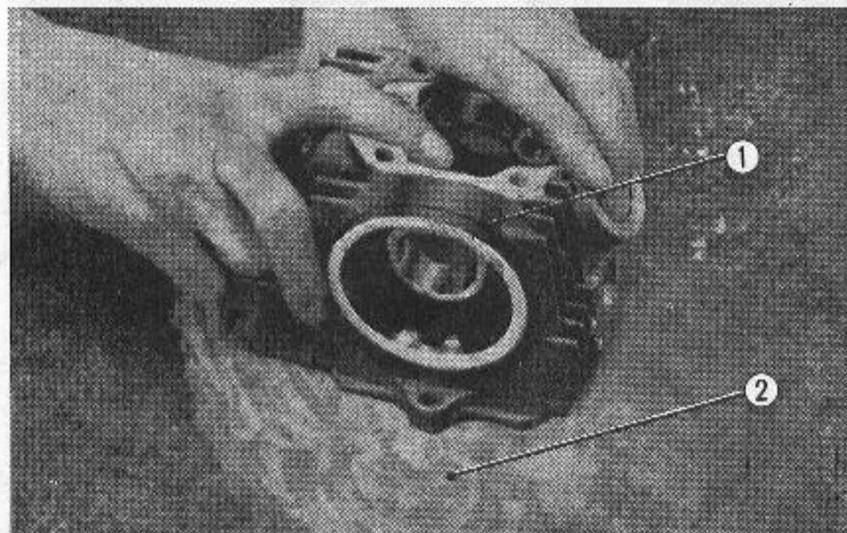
Zylinderkopf auf Wölbung prüfen
